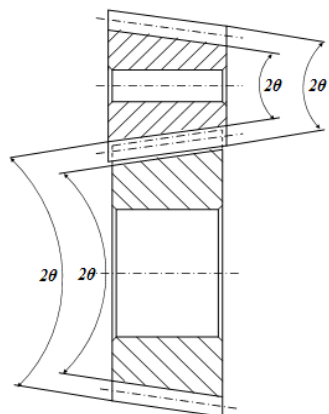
Схематичное изображение цилиндрической зубчатой пары Новикова со спрямленными зубьями
